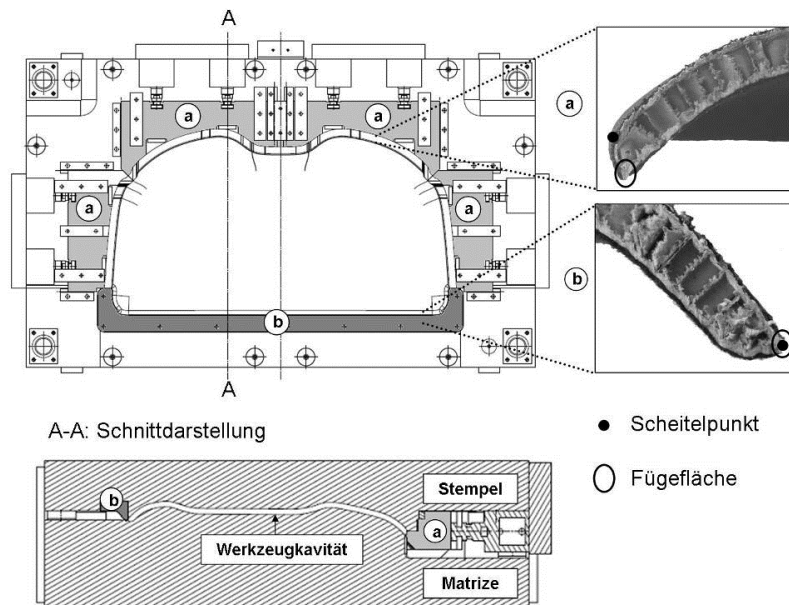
Schematischer Werkzeugaufbau mit weggesteuertem Werkzeugschließvorgang
